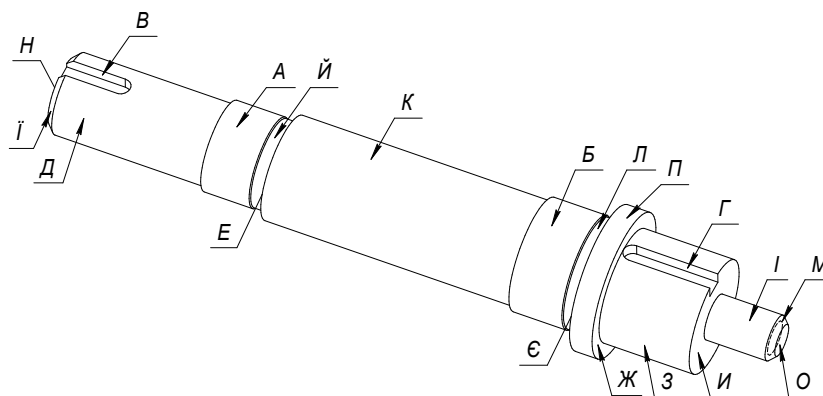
Позначення поверхонь деталі вал 5В.17.008
